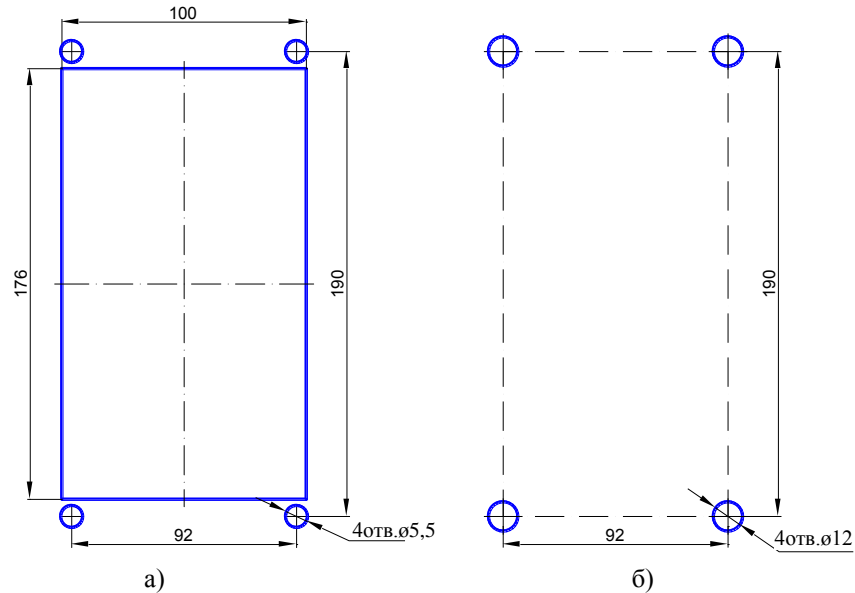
Разметка под крепление DP400-FDC24 а) снаружи; б) изнутри.
